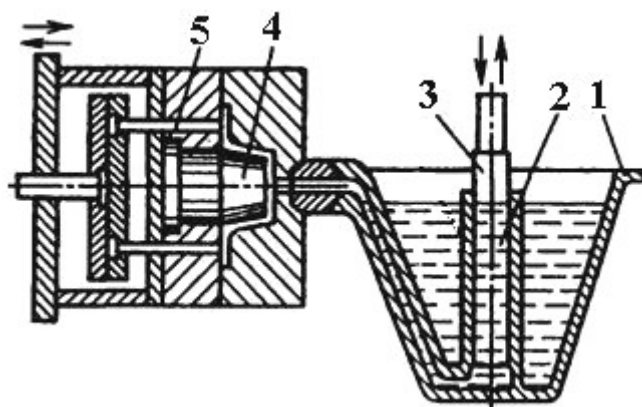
Схема процесса изготовления отливок на машинах с горячей камерой прессования: 1 – тигель; 2 – камера прессования; 3 – плунжер; 4 – полость пресс-формы; 5 – выталкиватели
